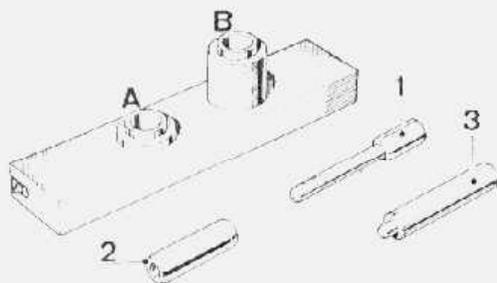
ferramenta especial T73L - 6135-A para remoção e instalação do pino do êmbolo
